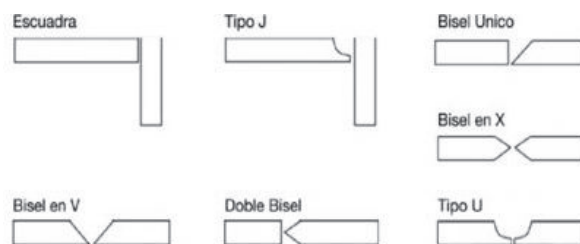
28 Biseles en los perfiles o planchas¹⁹
